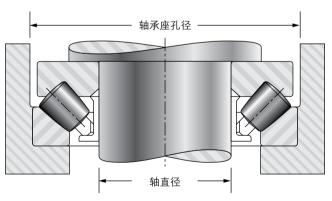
轴承座直径必须留出1.588mm (0.0625in.) 间隙,确保轴承 不承受径向载荷
